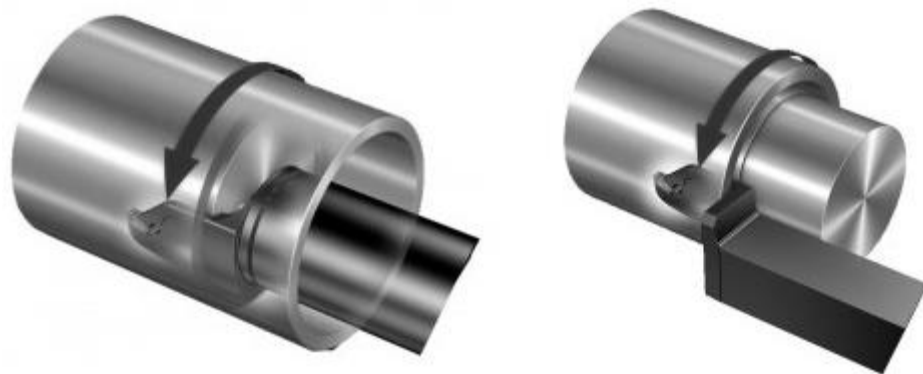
Схема конструктивного виконання типового інструменту для обробки торцевих канавок
